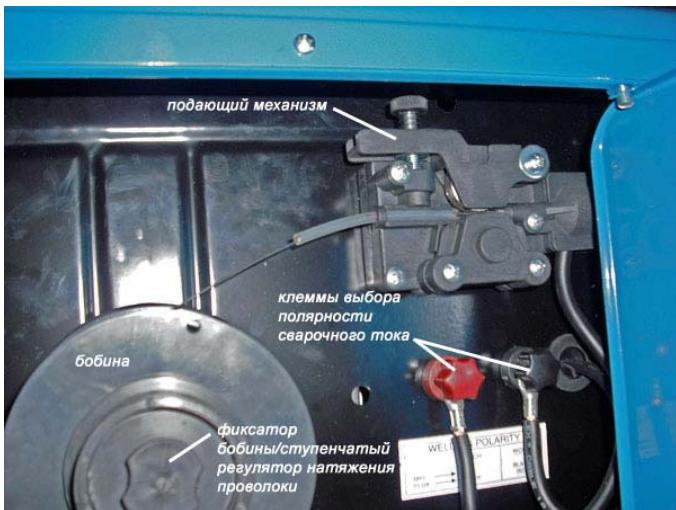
Подающий механизм и бобина сварочного полуавтомата Блю Велд 4.135
